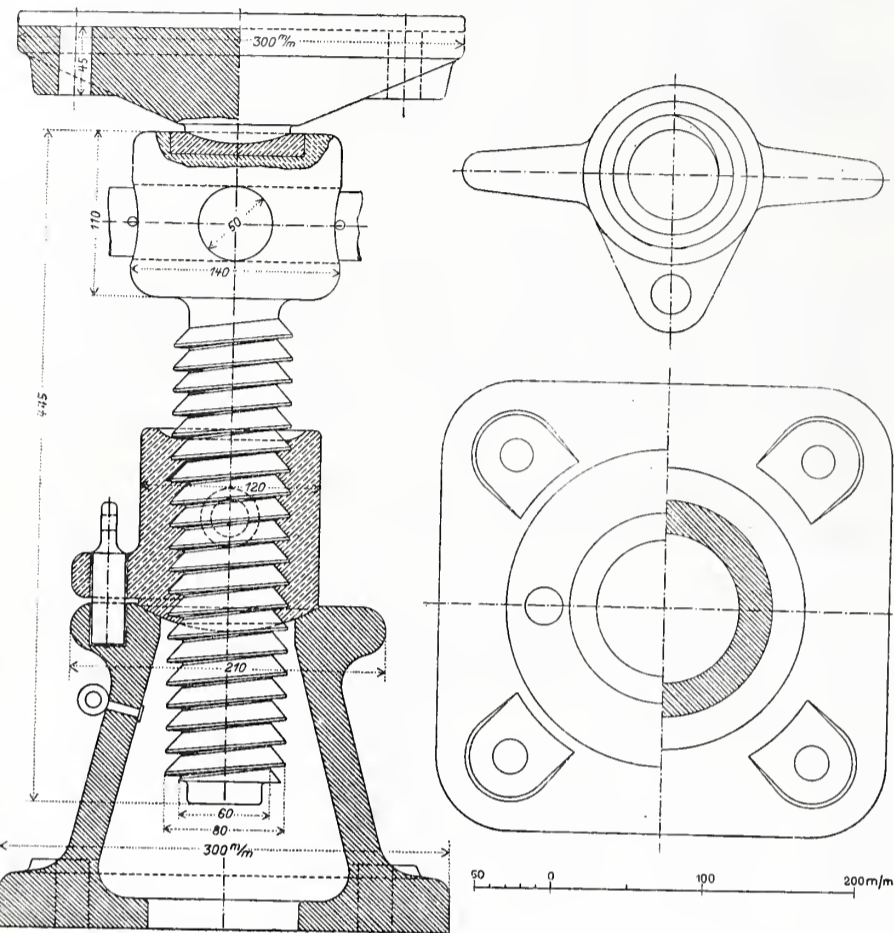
Senkschraube für das Lehrgerüst. — Masstab 1 : 6.
